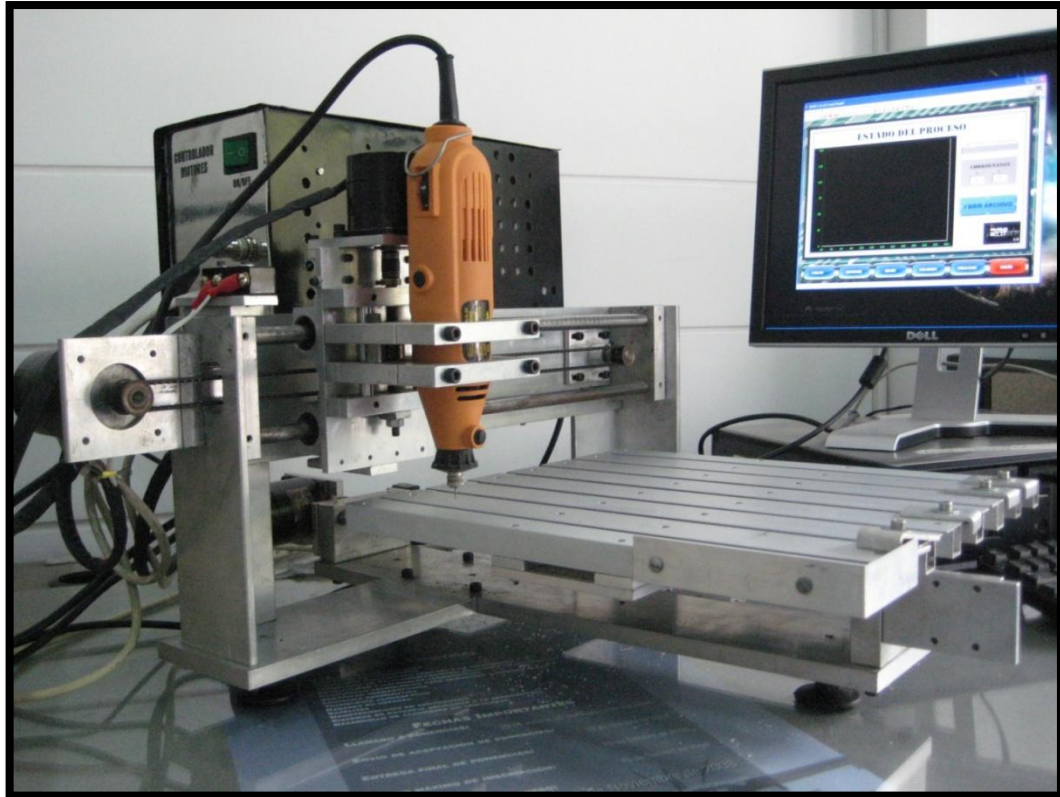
MÁQUINA CNC DRILL 1.0 [1]
